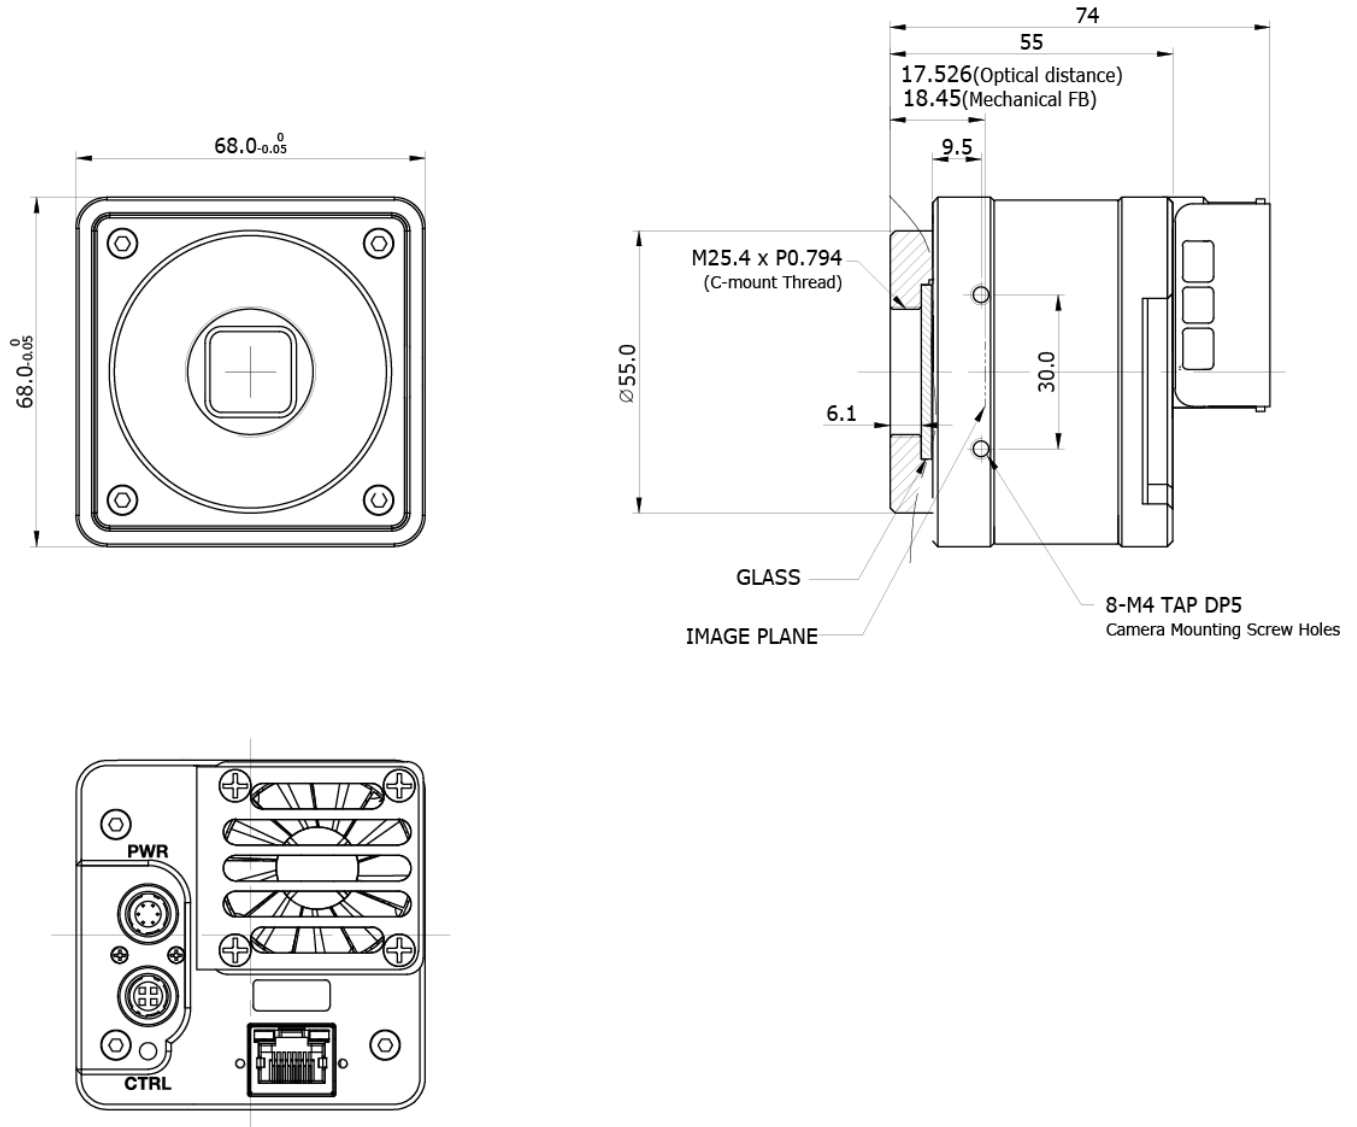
VC-25M10G-41I C-mount Mechanical Dimension
